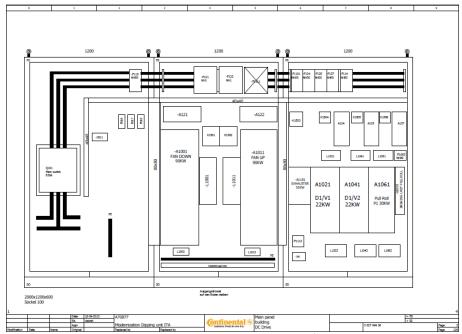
Configuração do quadro Benninger (EPLAN)
